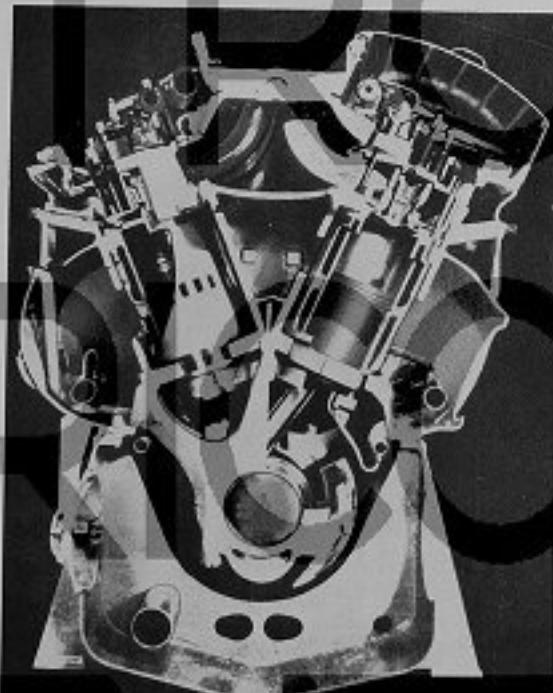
Sez. trasv. del motore GENERAL-MOTORS tipo 16-567 C
